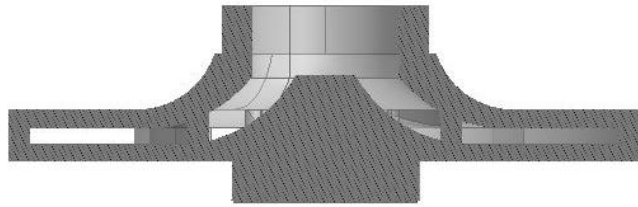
Geometria 3D. Vista lateral em corte (autor)
